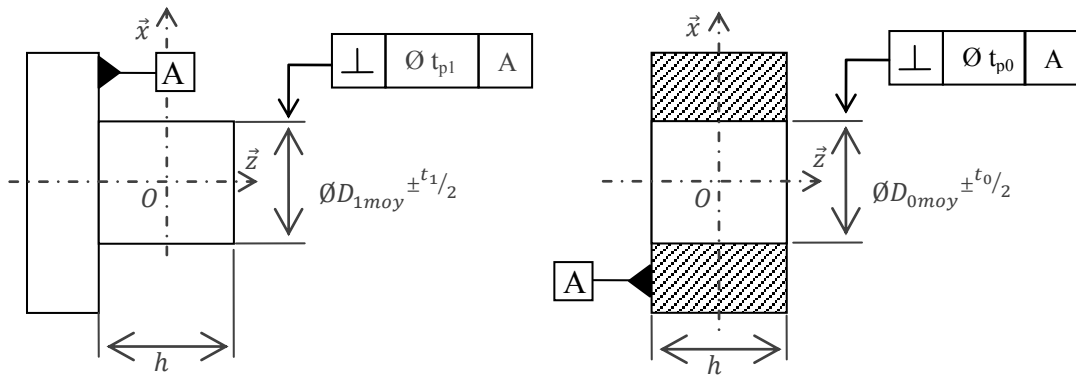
Tolérancement d'un assemblage plan/plan et cylindre/cylindre
